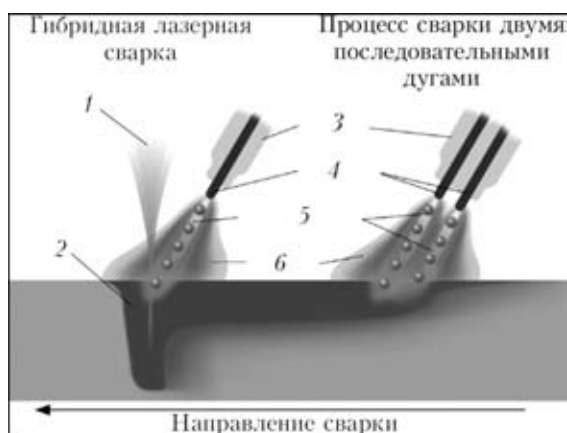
Гибридная лазерная сварка МИГ/МАГ + сварка двумя последовательными дугами (на материал воздействуют луч лазера и три дуги): 1 — луч лазера; 2 — зона сплавления; 3 — газовое сопло; 4 — электроды; 5 — импульсные дуги; 6 — защитный газ
